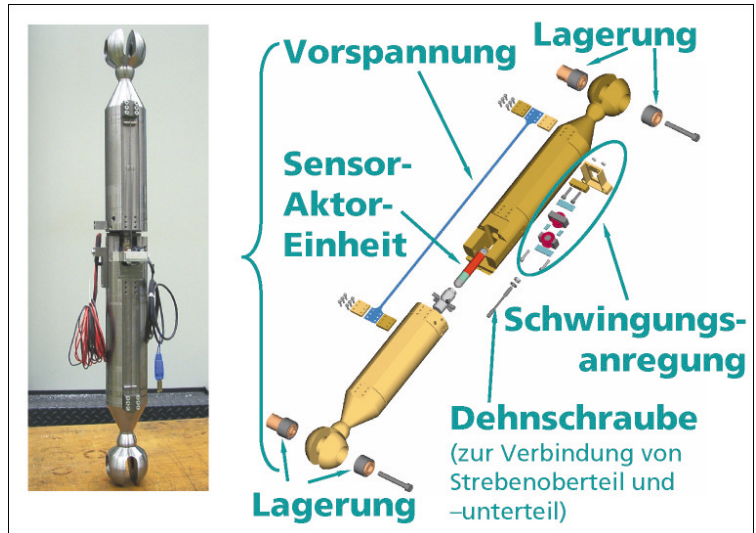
Gefertigter Prototyp und Explosionsdarstellung der Strebe
